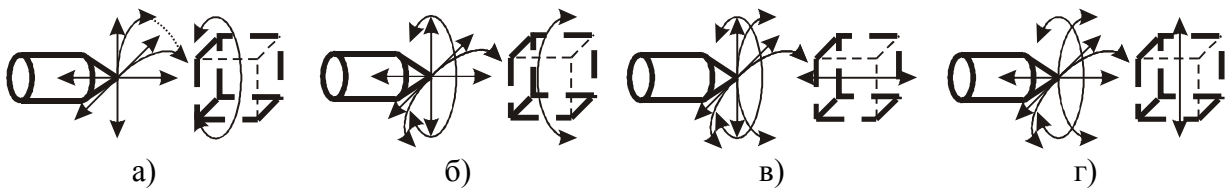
Схема напрямків руху інструмента у верстаті з комбінованими механізмами паралельної структури
